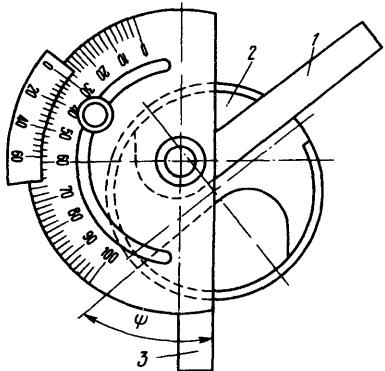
Измерение угла  $2\phi$  при вершине сверла универсальным угломером:
